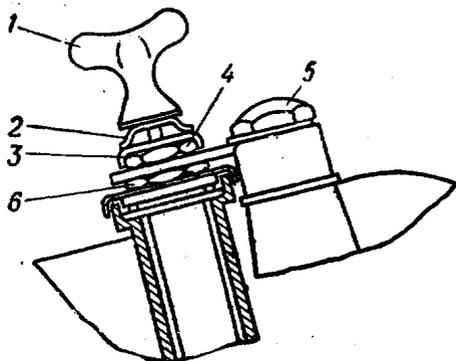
Регулировка подшипников рулевой колонки: 1 - барашек; 2 - пружинная шайба; 3 - опорная шайба; 4 - гайка стержня рулевой колонки; 5 - затяжные гайки; 6 - регулировочная гайка
